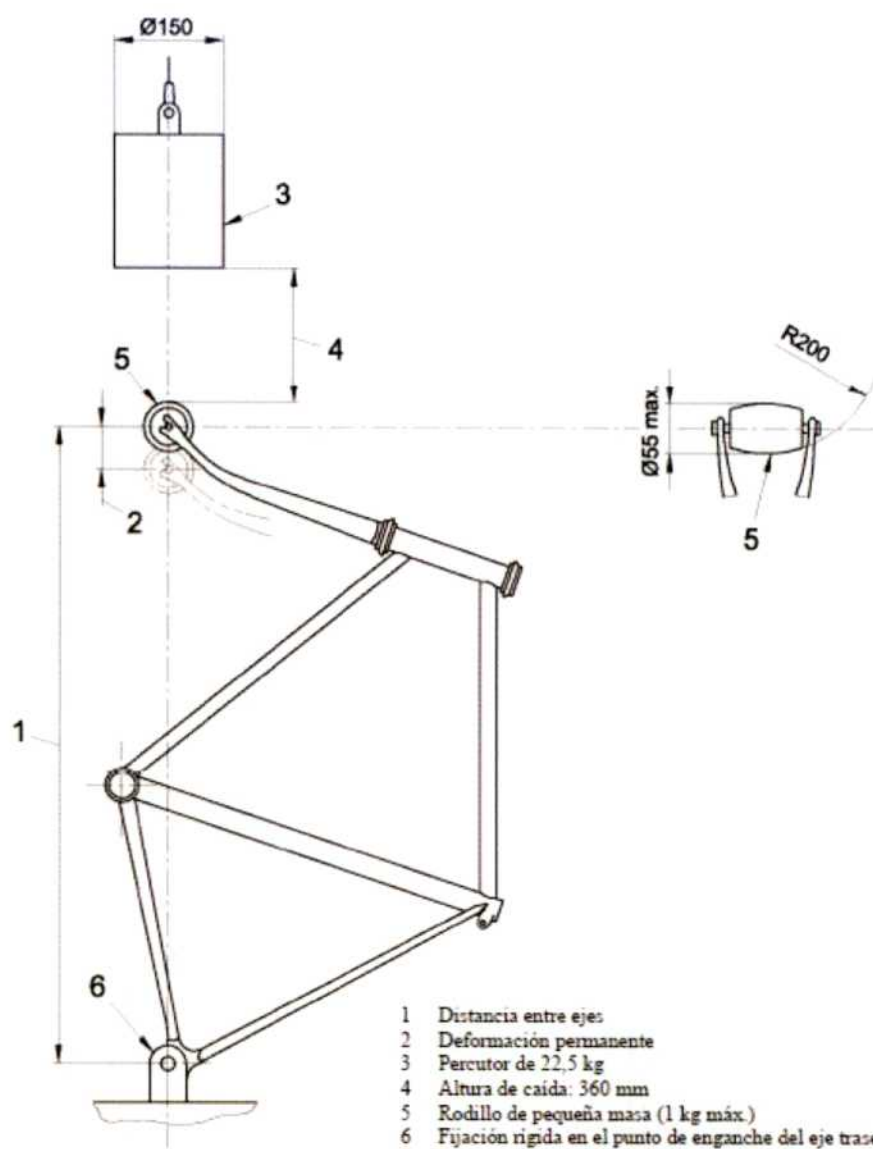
Conjunto cuadro y horquilla delantera. Ensayo de choque (caída de una masa).⁴⁶
